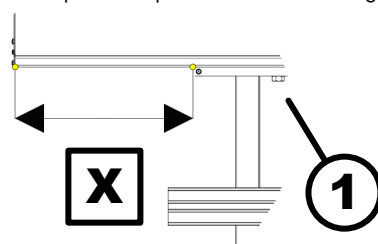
Detalle - Posición de montaje del carro escuadrador
